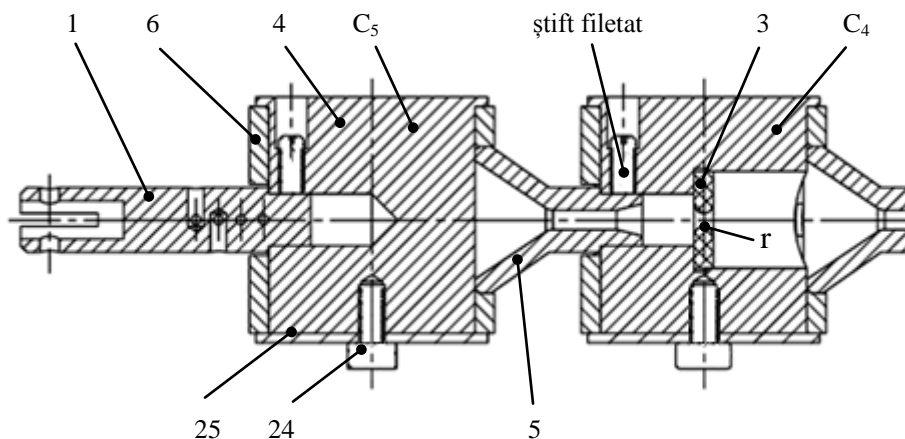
Secțiune longitudinală a cuplelor 5 și 4 (după planul B-B, rotit)
